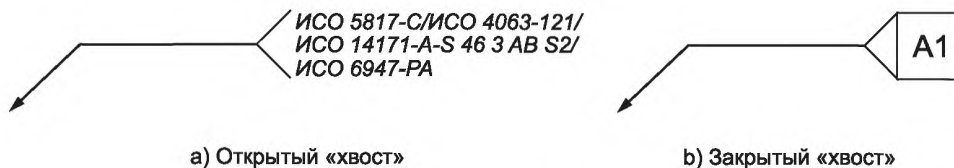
Примеры применения «хвоста» для условных обозначений сварного соединения
